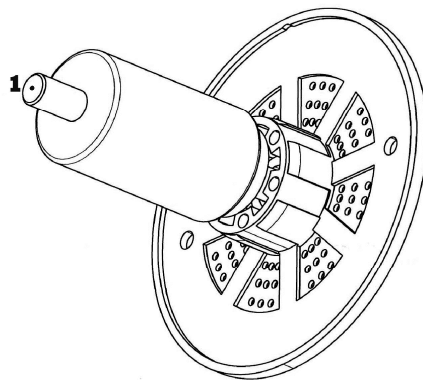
Rotor vom ECO Runner mit Abdeckplatte
